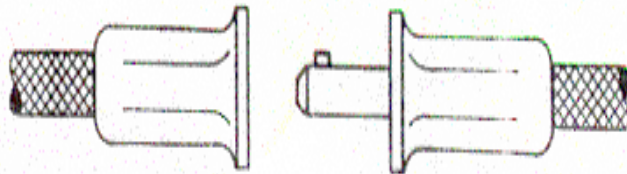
ACCESORIOS DE SOLDADURA – EXIGENCIAS Y MANTENIMIENTO
